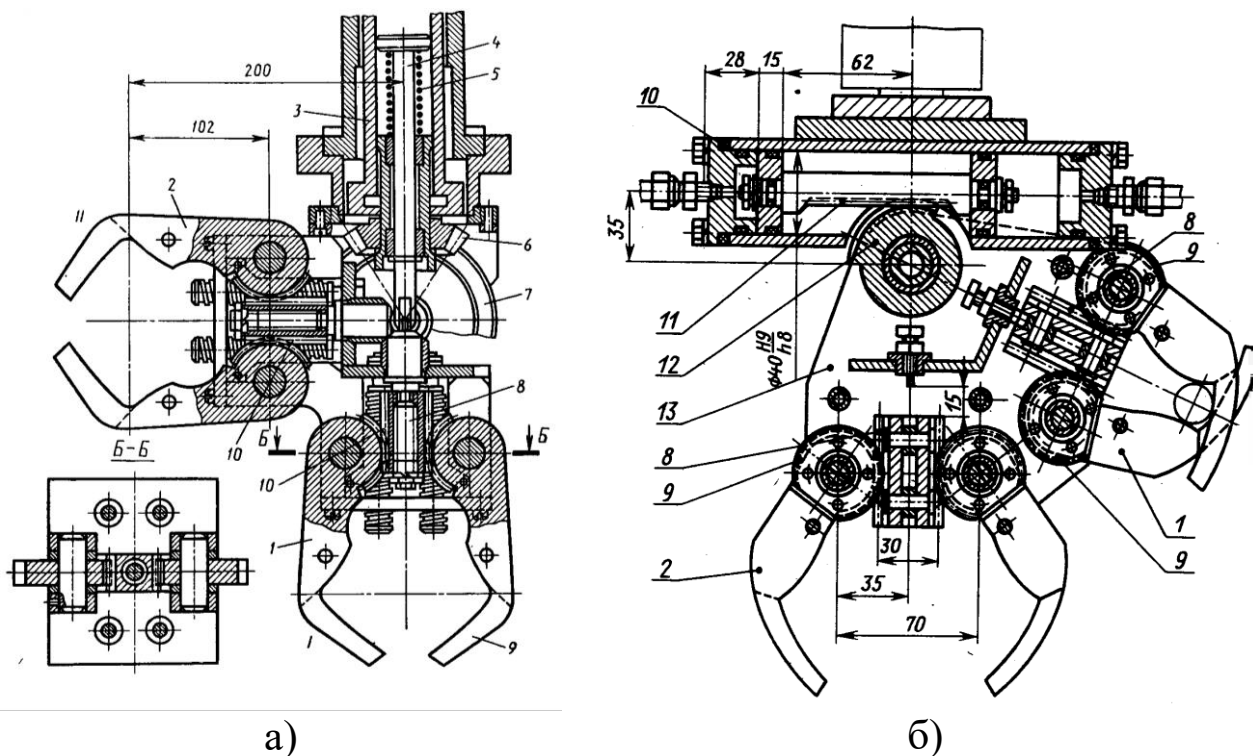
Двозахватні пристрої, захвати яких розташовані під кутом
